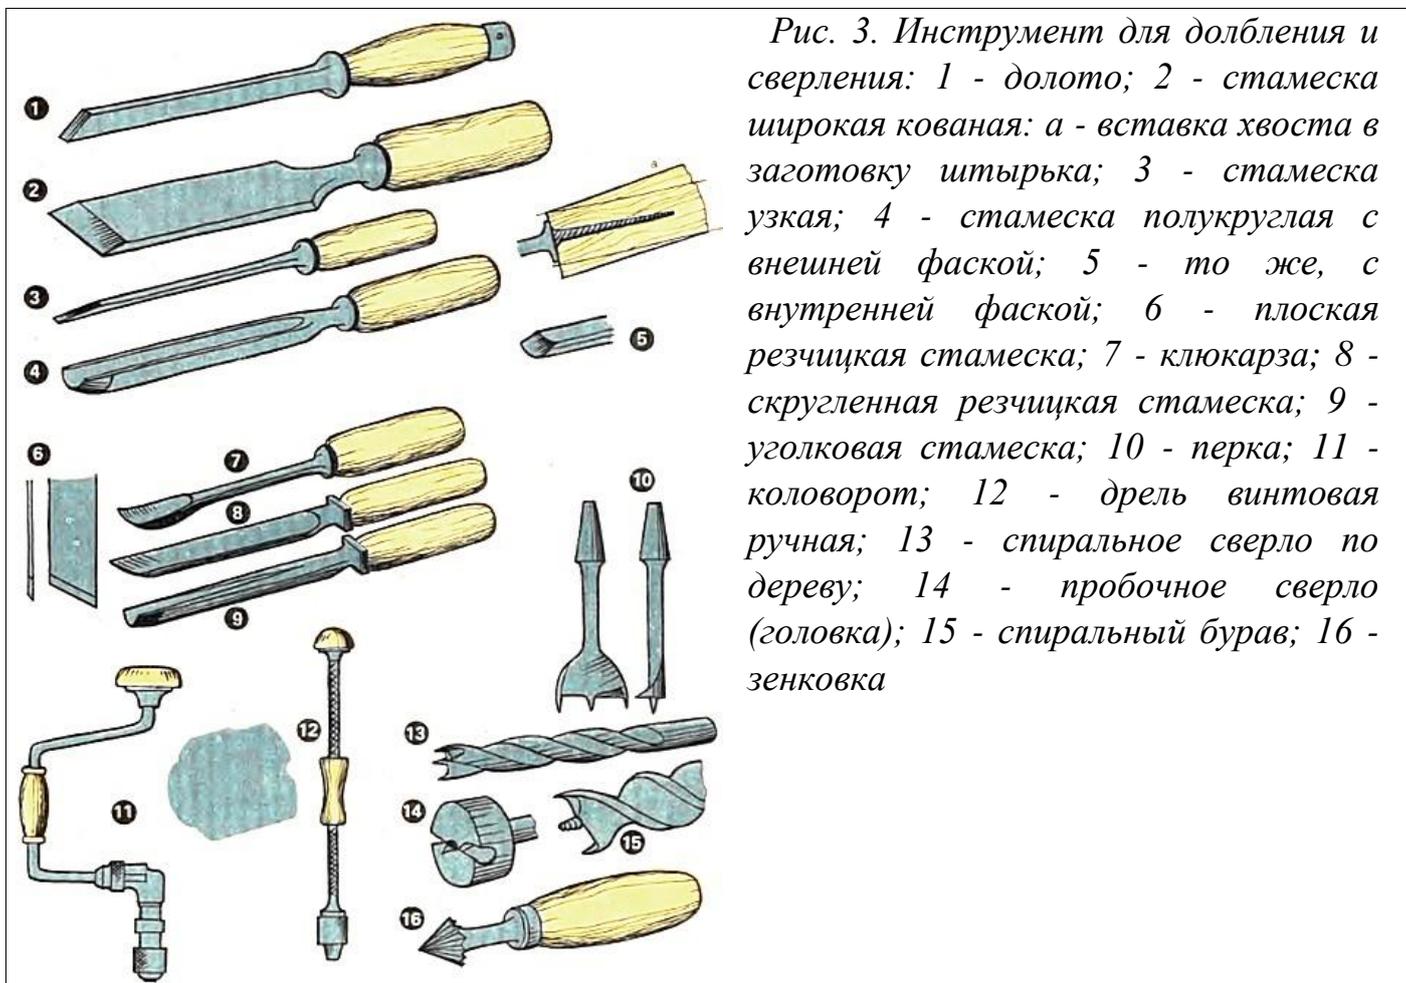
Инструмент для долбления и сверления: 1 - долото; 2 - стамеска широкая кованая; а - вставка хвоста в заготовку штырька; 3 - стамеска узкая; 4 - стамеска полукруглая с внешней фаской; 5 - то же, с внутренней фаской; 6 - плоская резчицкая стамеска; 7 - клюкарза; 8 - скругленная резчицкая стамеска; 9 - уголкового стамеска; 10 - перка; 11 - коловорот; 12 - дрель винтовая ручная; 13 - спиральное сверло по дереву; 14 - пробочное сверло (головка); 15 - спиральный бурав; 16 - зенковка
